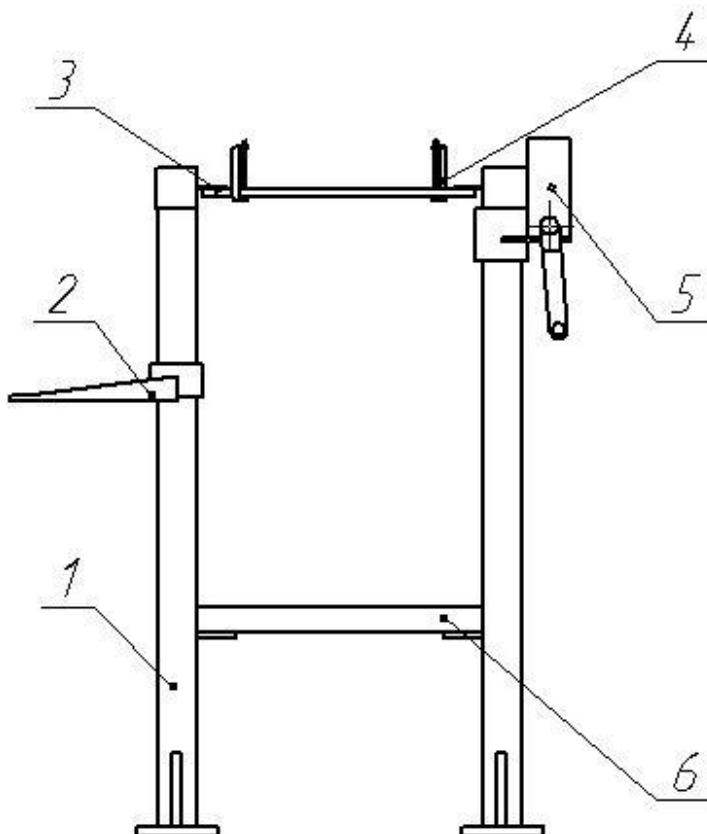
Схема стенда для разборки и сборки редукторов грузовых автомобилей ЗИЛ модель 3022.
